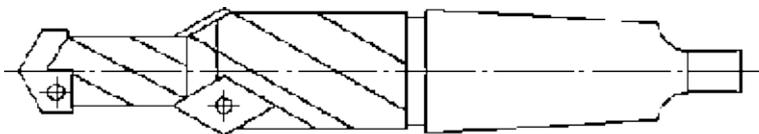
Сверло двухступенчатое со сменными пластинами
